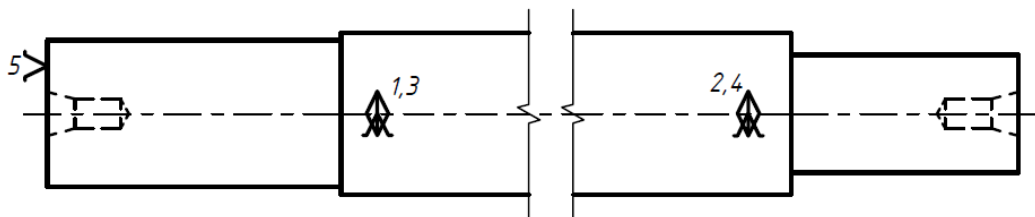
Схема базування при обробці торця штока і центрових отворів.
